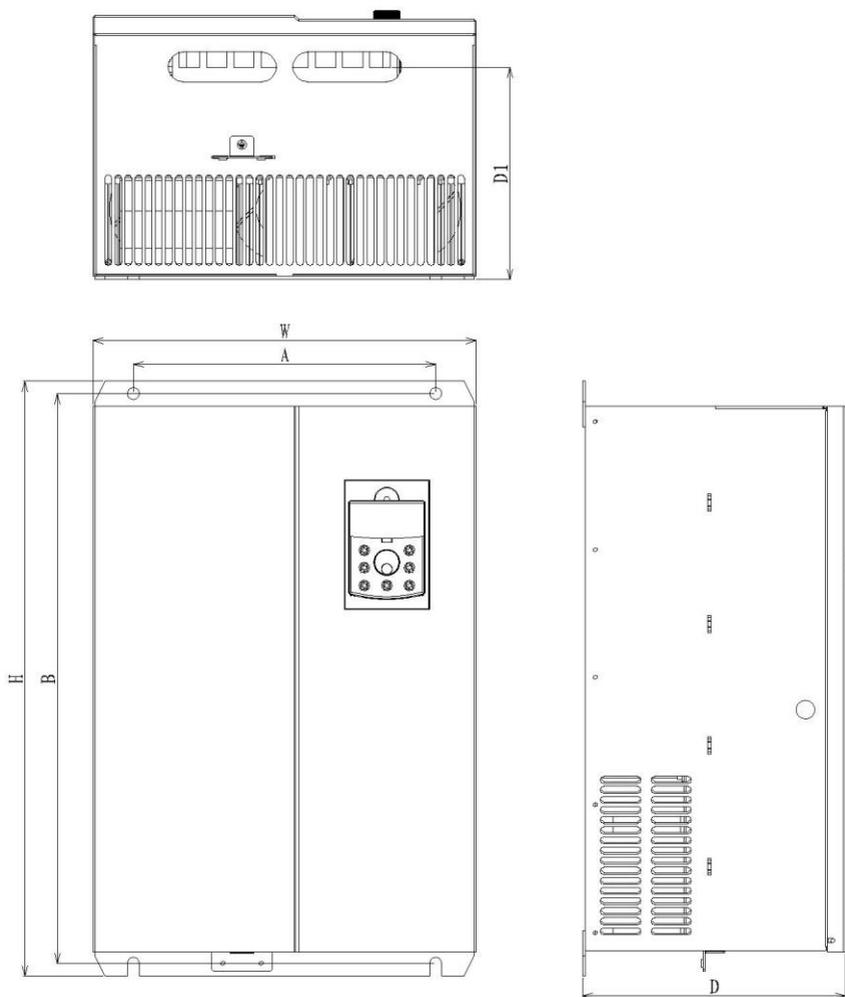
钣金件变频器外型尺寸及安装尺寸示意图
